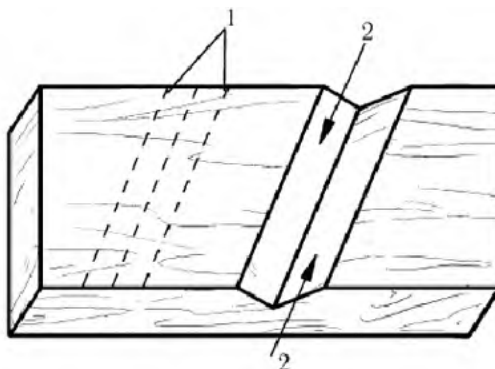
Выполнение двусторонней выемки, идущей по наклонной к направлению волокон заготовки (стрелками указано направление движения инструмента)
